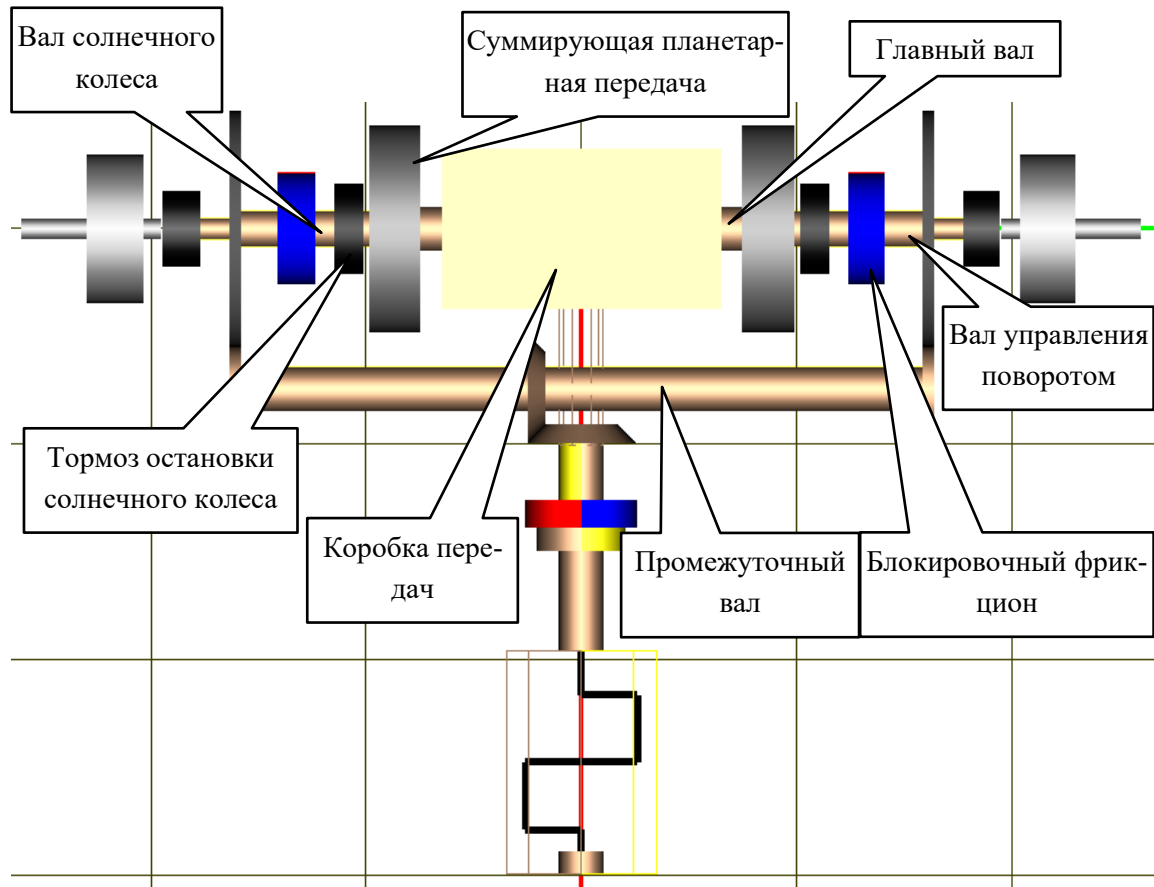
Двухпоточный механизм передачи и поворота 'Майбах'
